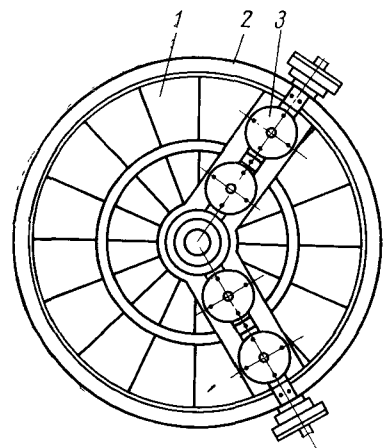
Экспериментальный дисковый регенератор фирмы Форд: 1 — матрица; 2 — корпус; 3 — уплотнение
